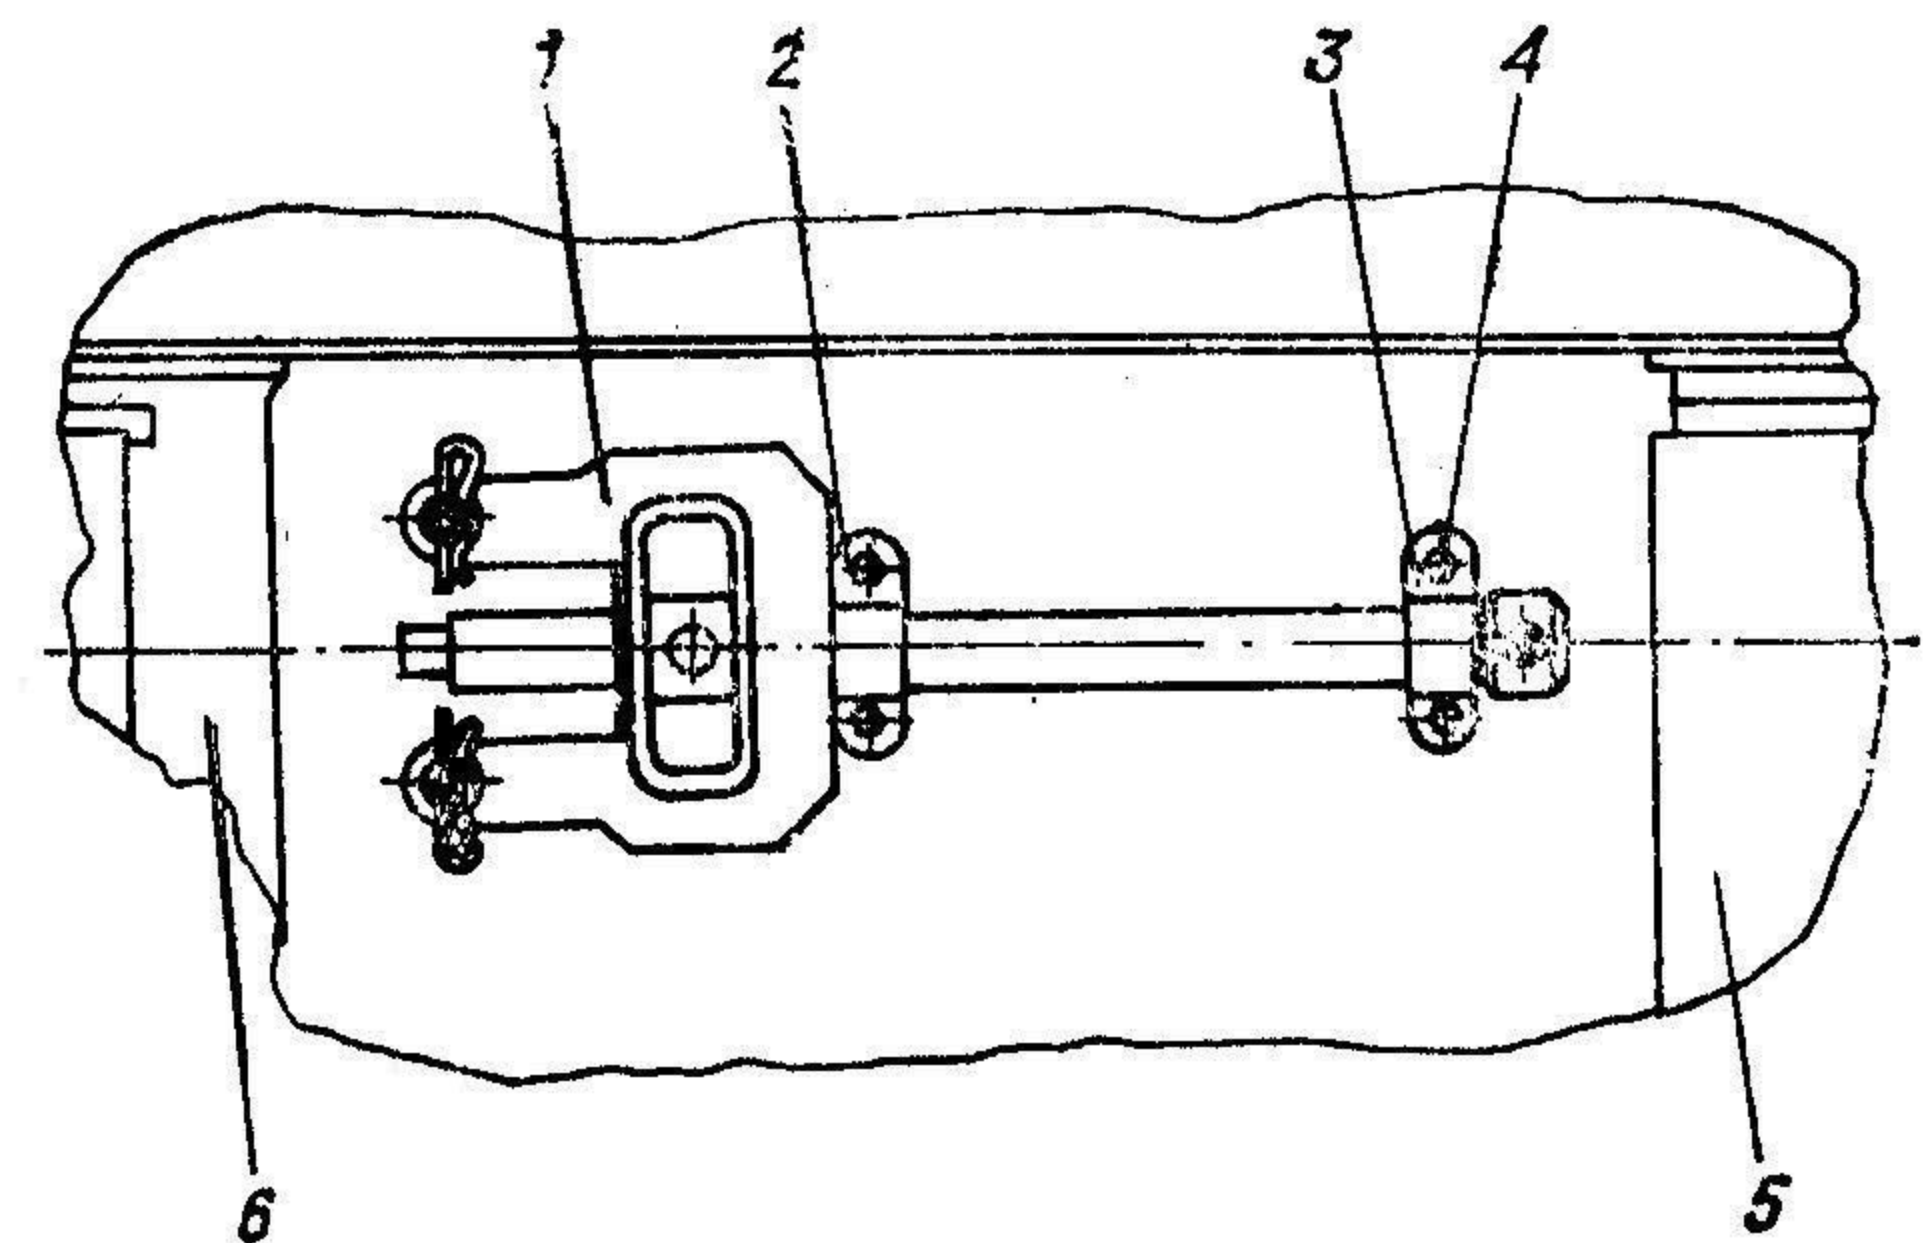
Установка приспособления для выпрессовки пальцев гусениц:
